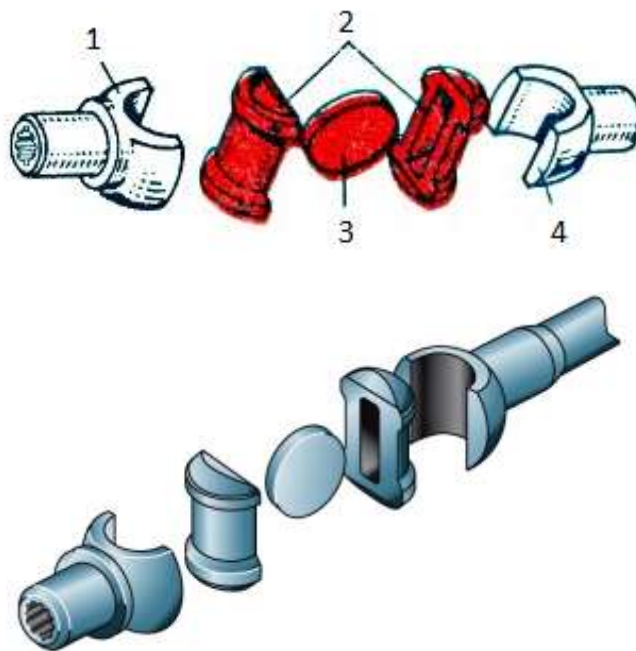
Кулачково-дисковий шарнір [5]:
